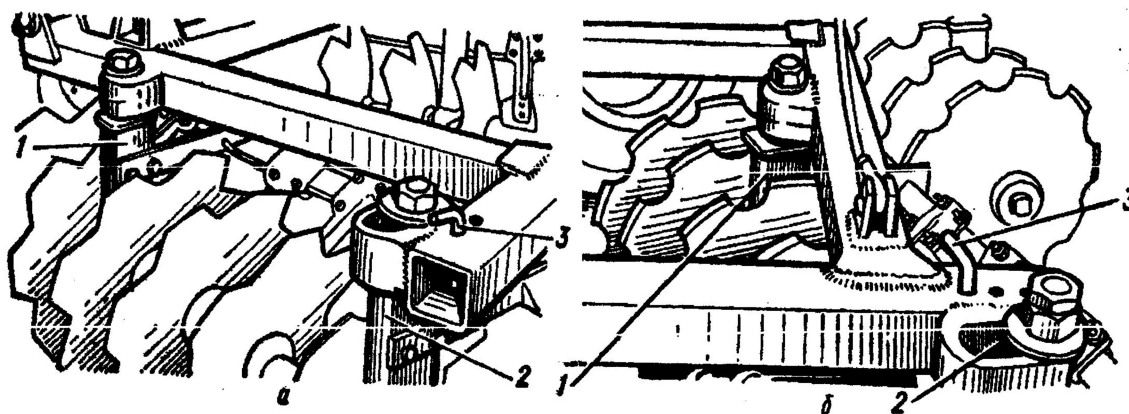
Пристрій для регулювання кута атаки батарей дискової борони БДВ-7:
